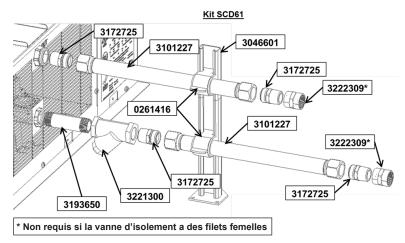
Suggestions d'assemblage pour la trousse à eau expédiée séparément
